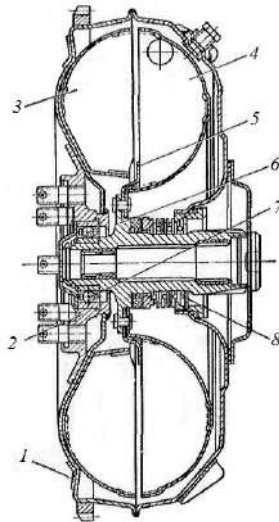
Гідромуфта: 1 – корпус; 2 – маточина; 3 – колесо насоса; 4 – колесо турбіни; 5 – порогова шайба; 6 – вал турбіни; 7 – шарикопідшипник; 8 – ущільнення
